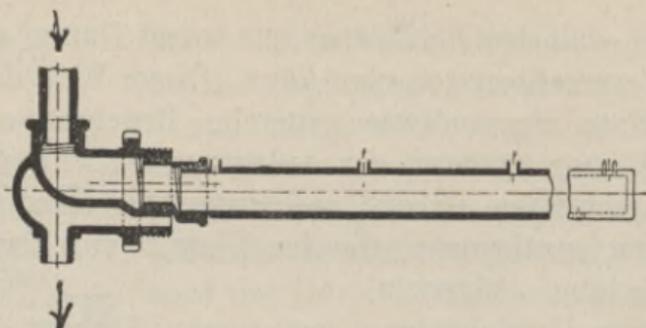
Anschlußstück mit Düsenrohr für Luftumwälzung.
